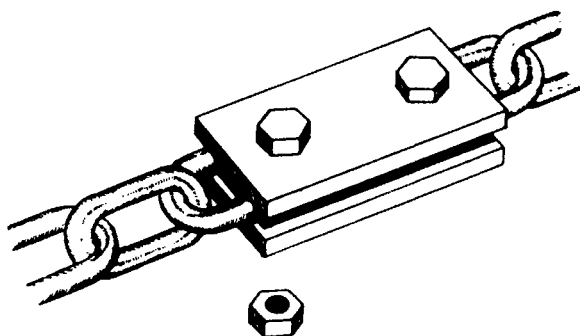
Assemblage pour chaîne fait de deux plaques
